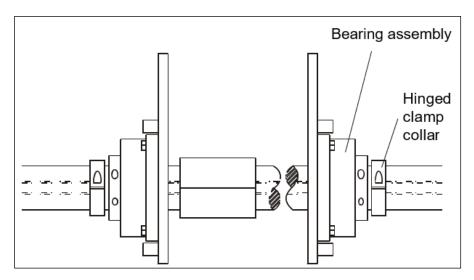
MONTAJE DE SOPORTE DE RODAMIENTO DE MONTAJE DI (IZQUIERDA) Y ABRAZADERA CON BISAGRA (DERECHA)
